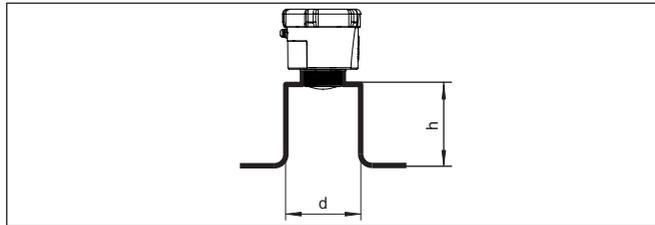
Montage de la rehausse en cas de dimensions de rehausse différente
